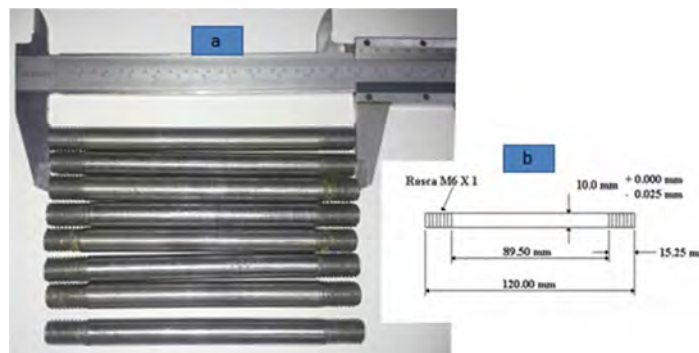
Corpos de prova usinados (a), à esquerda, e croqui (b), à direita.
